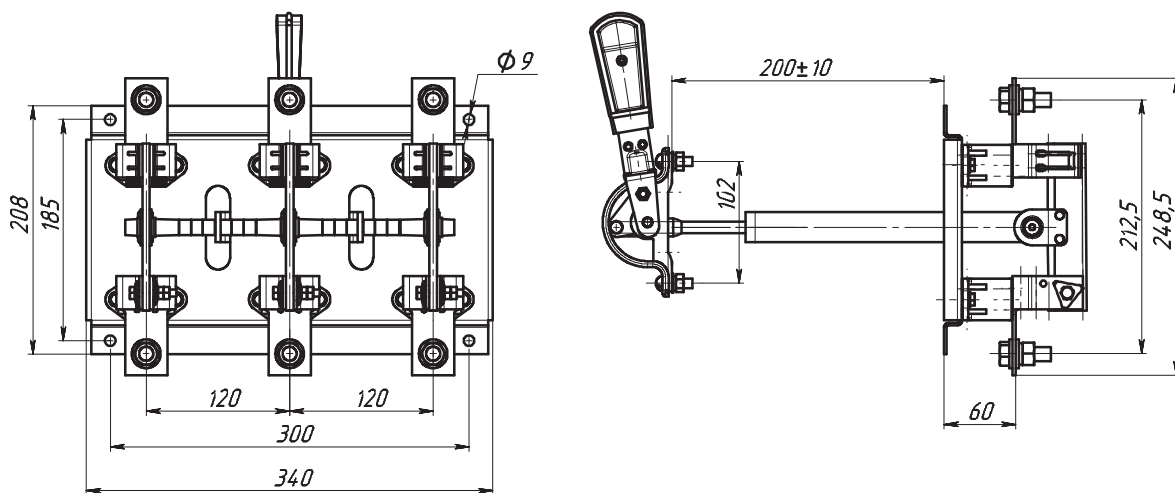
Разъединитель серии Р с центральным приводом, РЦ-6 на номинальный ток 630 А
